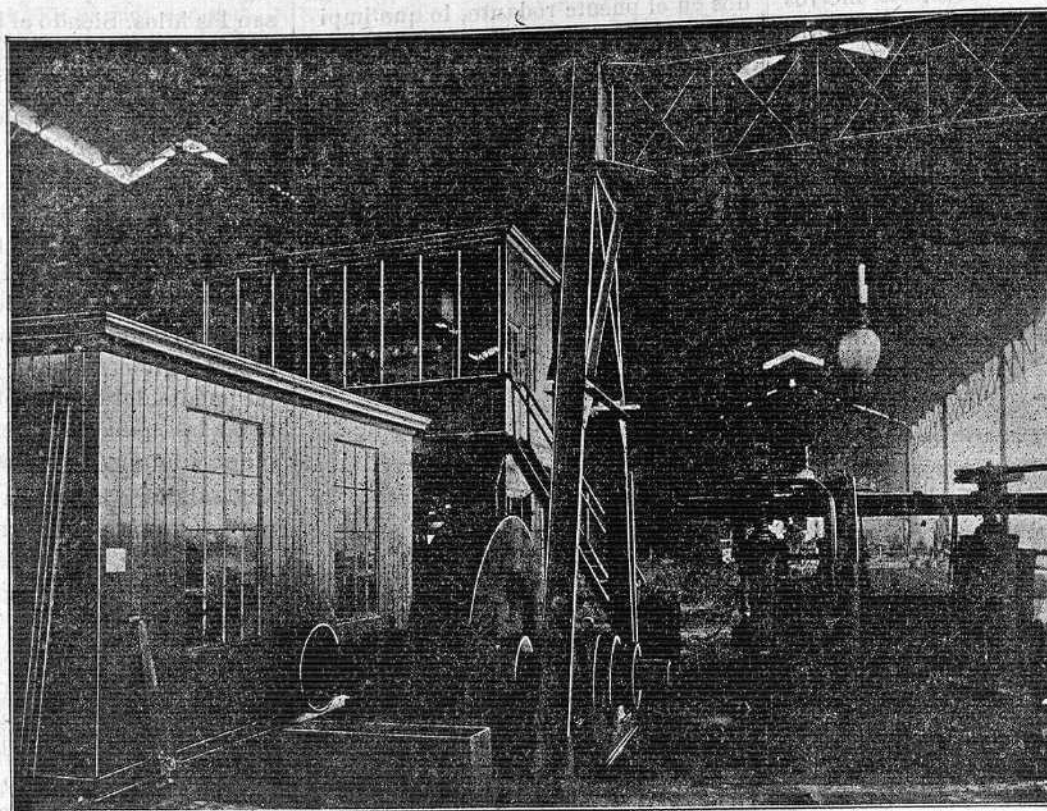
LAMINADOR ACCIONADO POR UN MOTOR WESTINGHOUSE DE MONTAJE DIRECTO.
